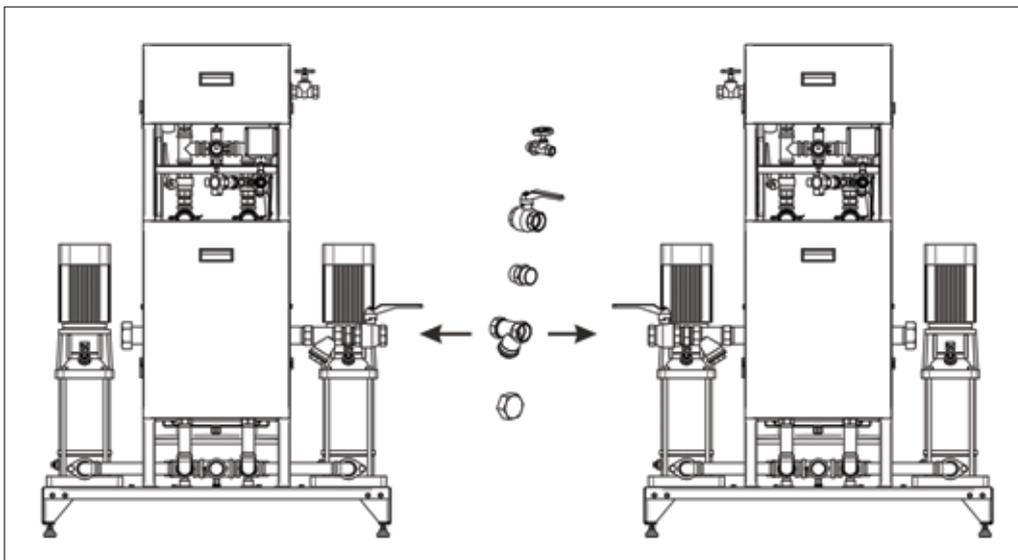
Umbau Anschlussseite Hydraulik MULTICONTROL MODULAR
